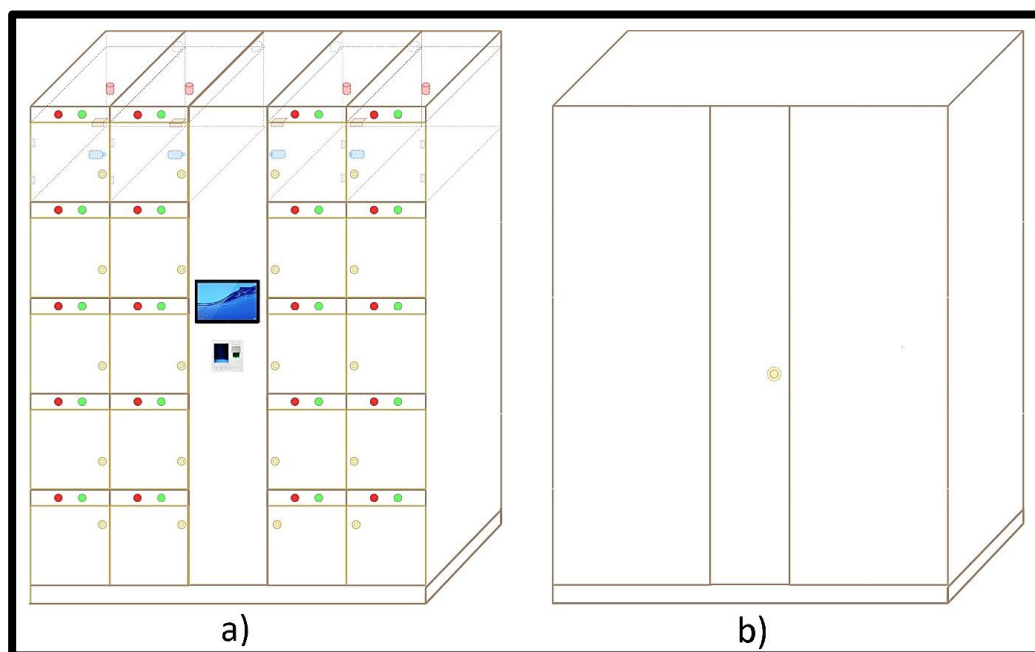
Estructura del sistema de gestión de proyectores a) Frontal. b) Posterior.
